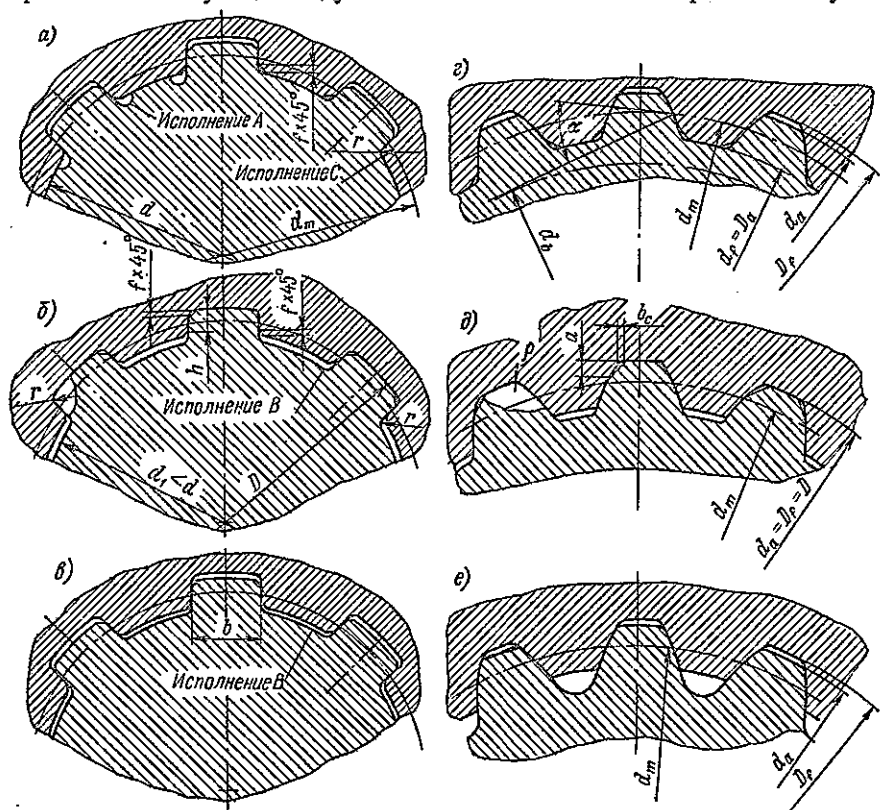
Шлицевые соединения с прямобочными и эвольвентными профилями
